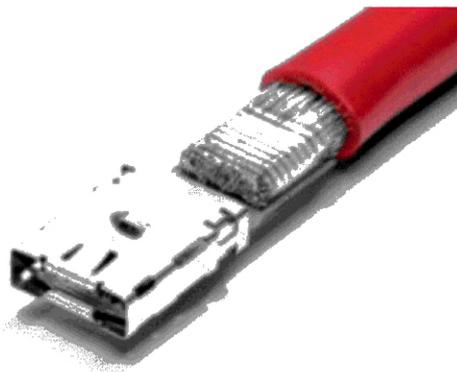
Пример 2 ультразвуковой сварки на наконечнике
